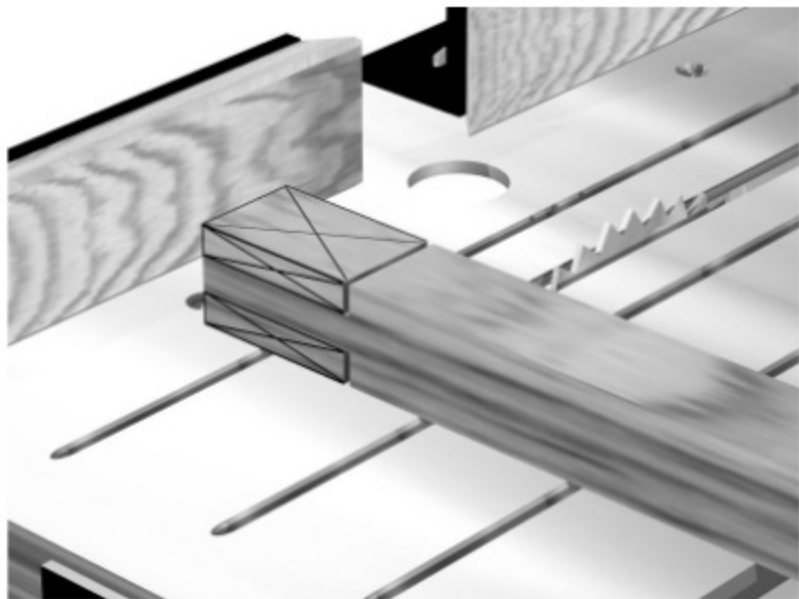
Los primeros cortes se realizan con la pieza plana y apoyada en la guía transversal
